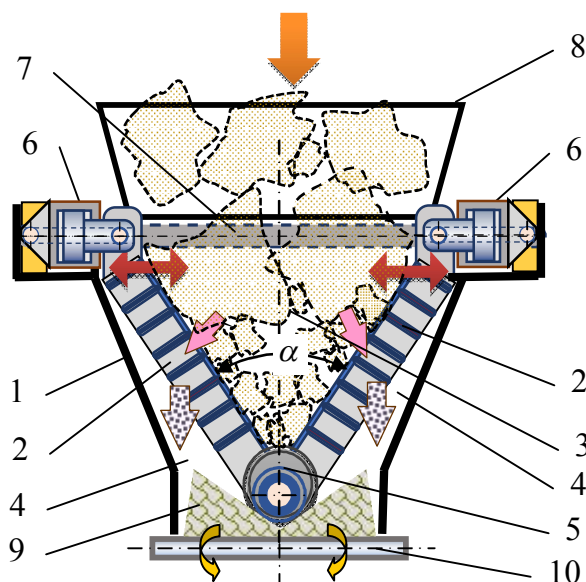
Новая конструктивная схема симметричной ударной щековой дробилки с гидроприводом и дробящими плитами колосниковой конструкции
